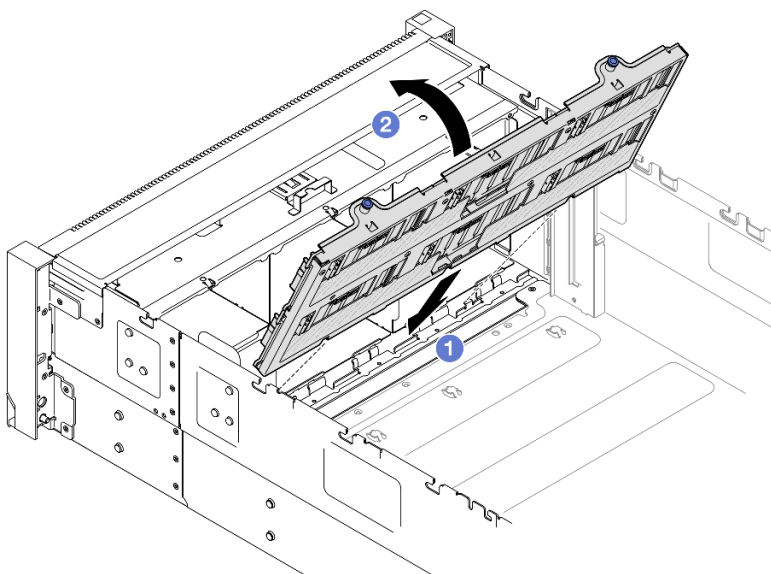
Instalando um conjunto de portadora do backplane da unidade
